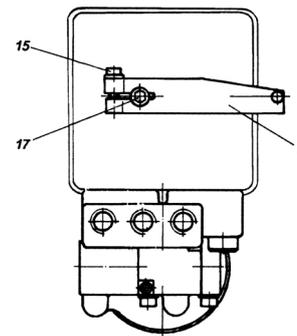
Fixação da alavanca de realimentação ao posicionador
